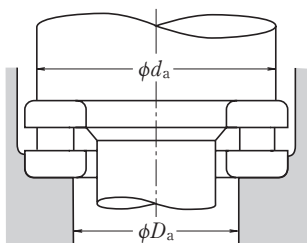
Диаметры опорной поверхности для упорных роликоподшипников
